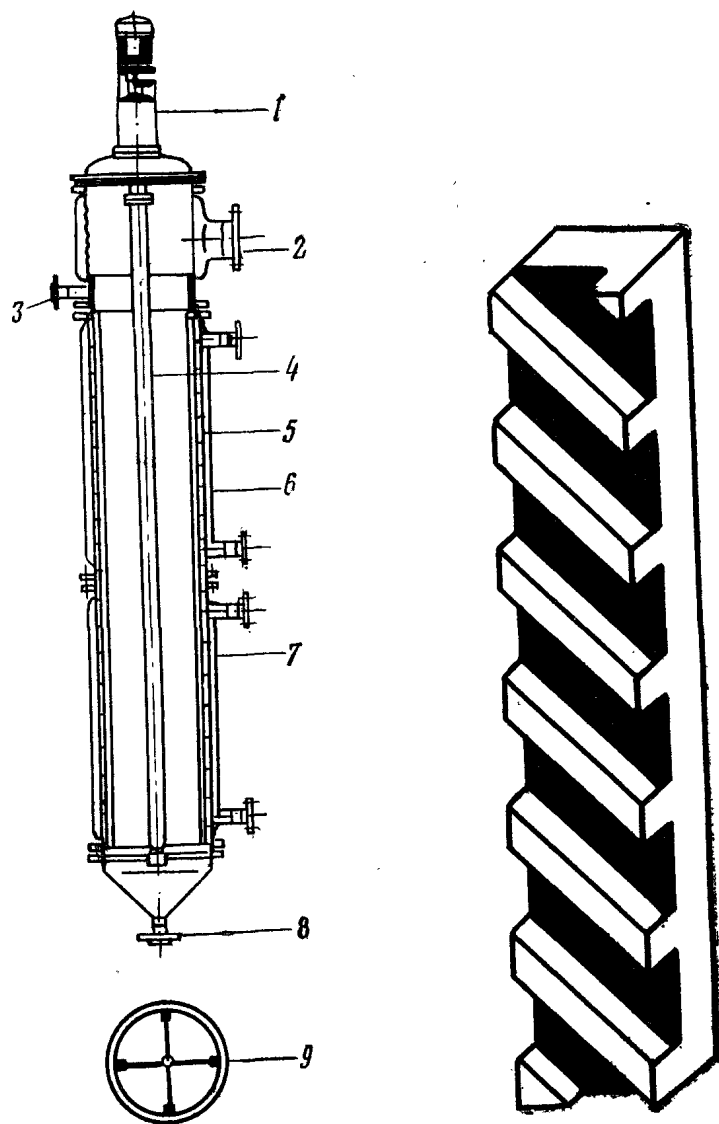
Пленочный испаритель с роторной мешалкой и подвижными косозубыми скребками
